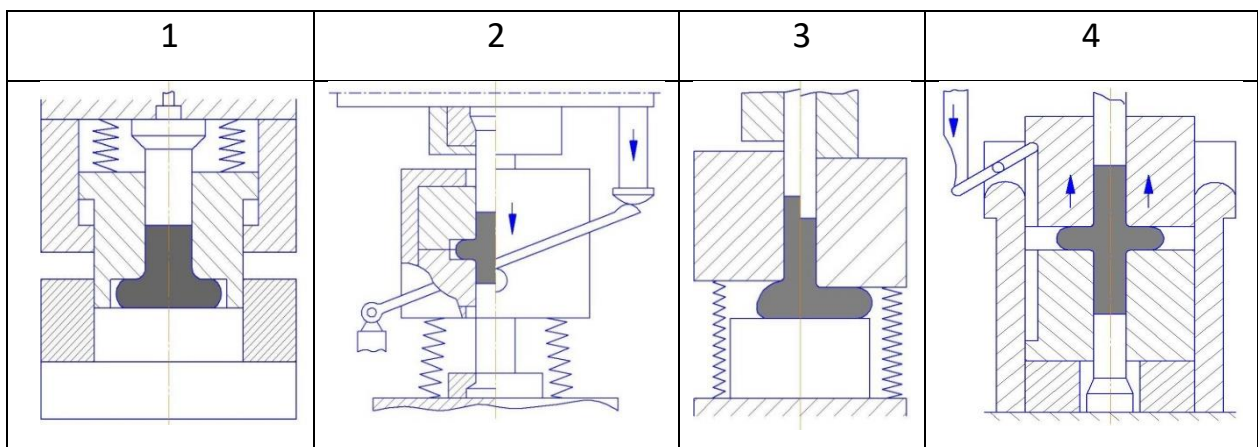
Типові схеми компоновки штампів с роз'ємними матрицями
